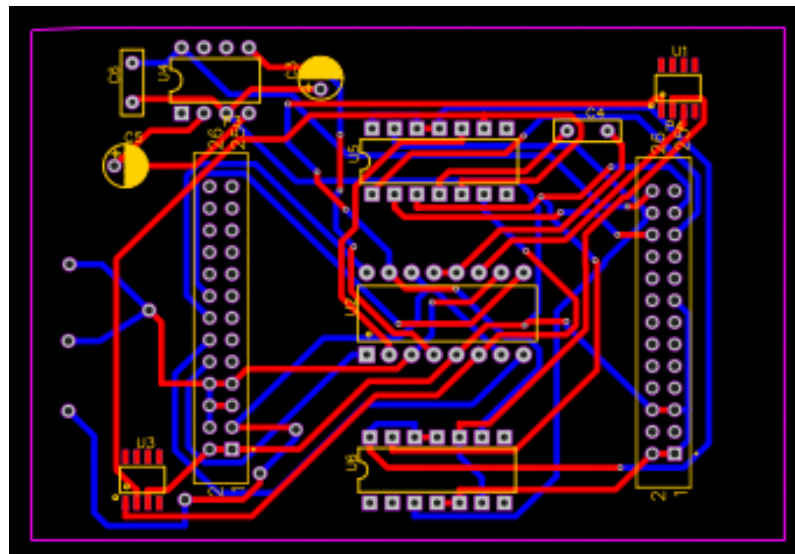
Schéma du PCB de la carte de TP 2 généré par EASYEDA
